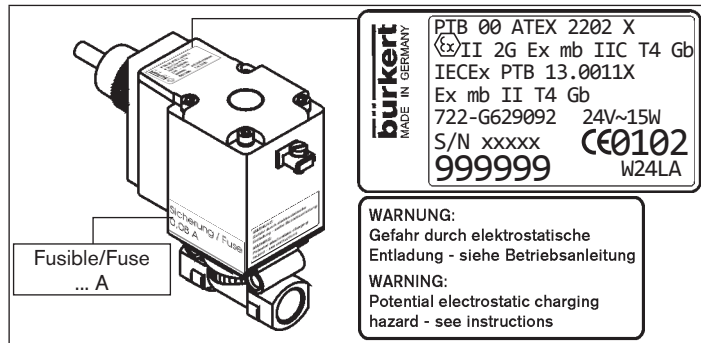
Exemple de plaque signalétique pour une bobine de type 7...-
